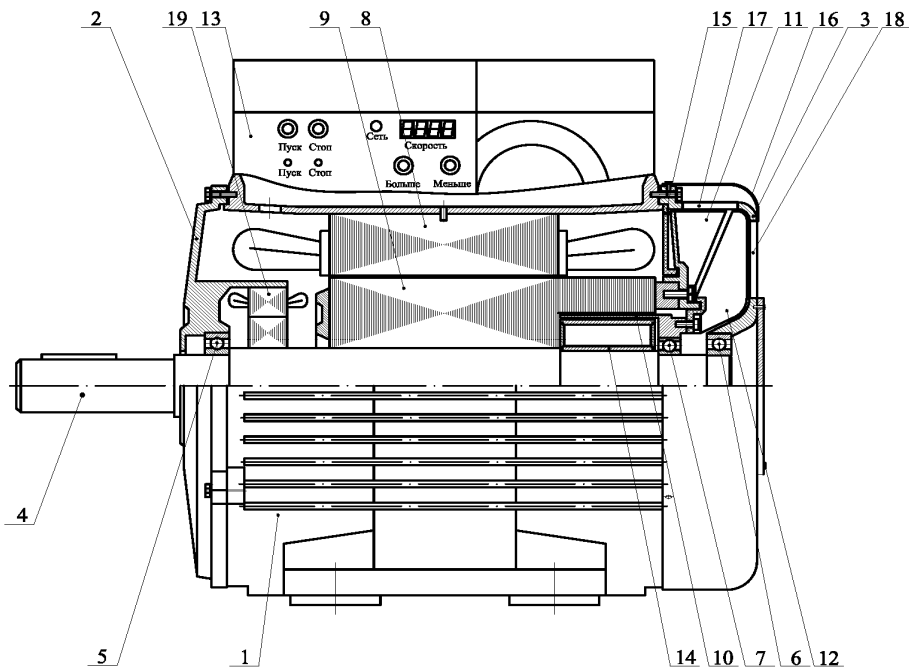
Особенности конструкции асинхронного электродвигателя по конструктивной схеме ДАС с двухроторной электромеханикой (ДАС-12): 1 – станина электродвигателя; 2, 3 – подшипниковые щиты; 4 – вал силового ротора; 5, 6 – подшипники силового ротора; 7 – подшипник малого ротора; 8 – магнитопровод статора с обмоткой; 9 – удлиненный магнитопровод силового ротора со стержневой обмоткой; 10 – малый ротор вентилятора; 11 – вентилятор-теплорассеиватель, закрепленный на силовом роторе; 12 – вентилятор, закрепленный на малом роторе; 13 – клеммная коробка со встроенным электронным блоком регулирования; 14 – магнитопровод малого ротора вентилятора; 15 – кольцевая перегородка; 16 – кожух; 17 – осевые отверстия подшипникового щита для вывода охлаждающего воздуха из электродвигателя; 18 – радиальные отверстия подшипникового щита для ввода охлаждающего воздуха в электродвигатель; 19 – датчик скорости
